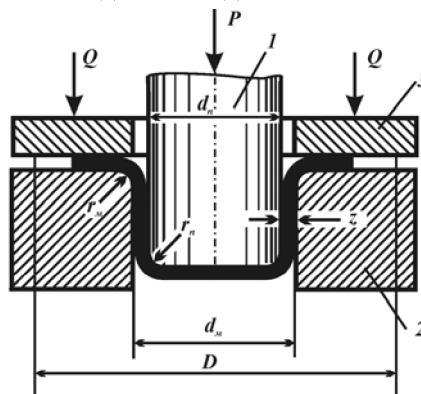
Схема вытяжного штампа с прижимом плоской заготовки (первая операция вытяжки):
